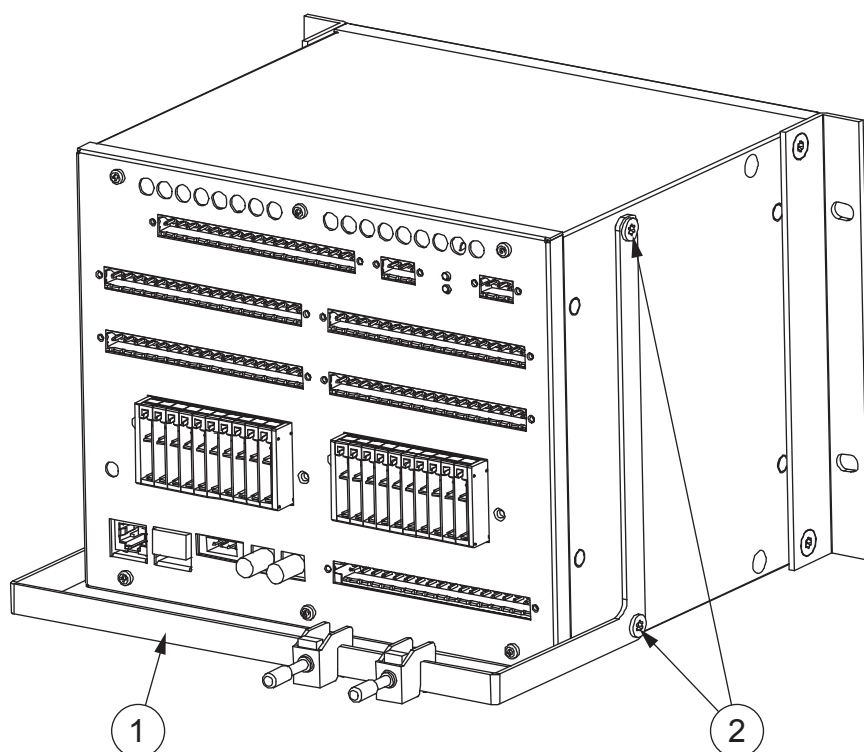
Unidad principal 4U con rail opcional de pantallas de cables montado
